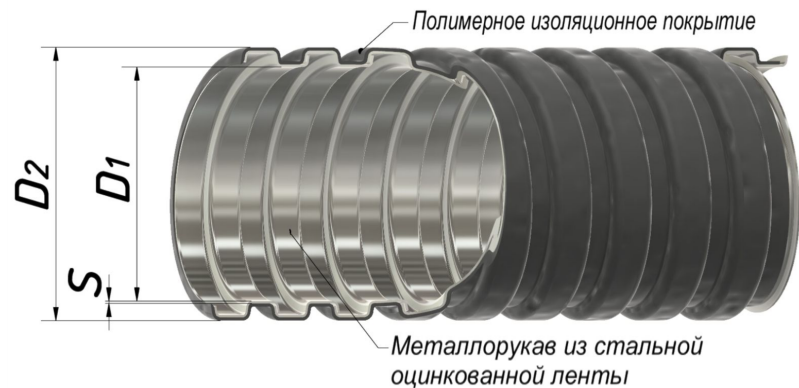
Металлорукав типа РЗ-ЦП нг с протяжкой
